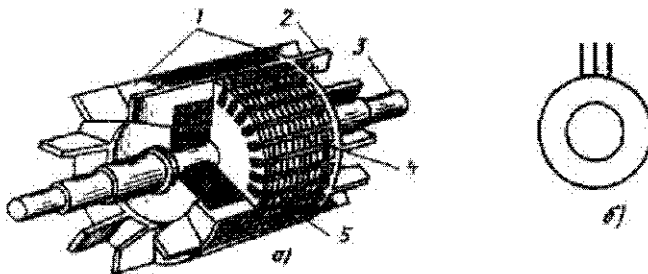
Конструкция (а) и условное графическое обозначение (б) ротора с короткозамкнутой обмоткой; 1 - замыкающие кольца; 2 - вентиляционные лопасти; 3 - вал; 4 - пакет ротора; 5 - стержни обмотки
